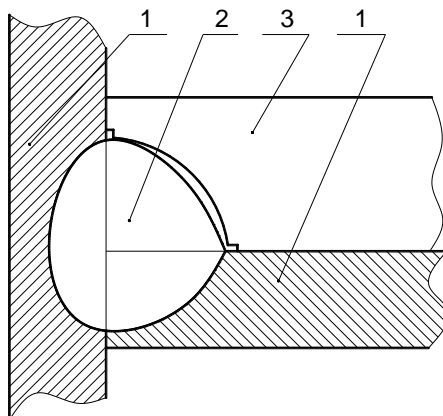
Схема контролю геометричних розмірів зварного шва за допомогою щупа
